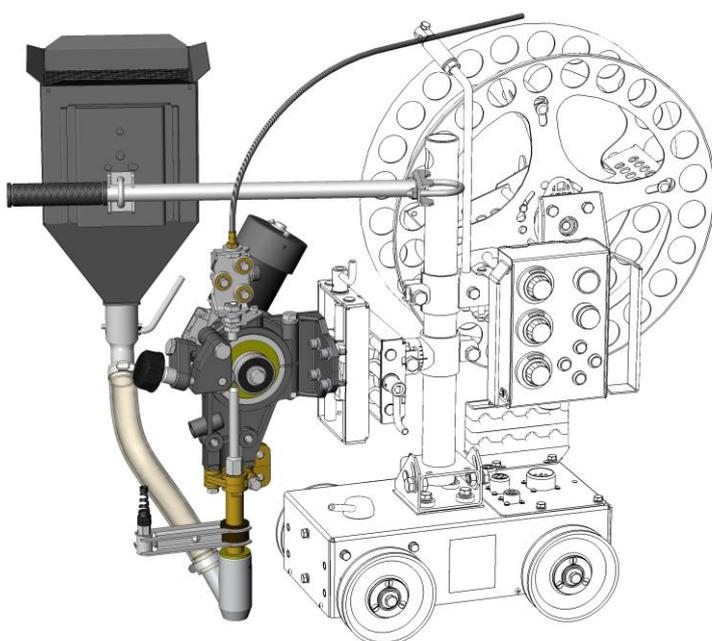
Комплект сварочной головки АДФ-1000 для сварки под флюсом проволокой $\varnothing 1,2-2,4$ мм.
